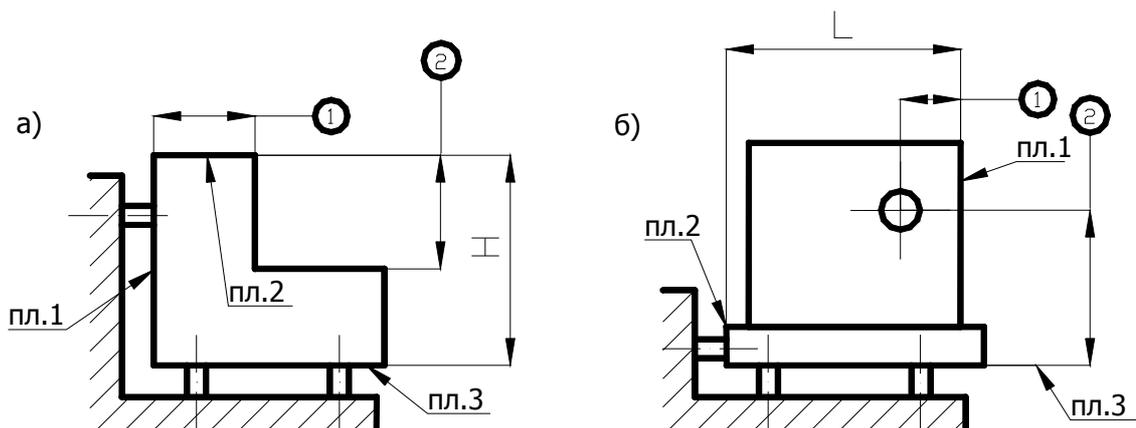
Базирование заготовки при фрезеровании углового паза (а) и сверлении отверстия (б).
